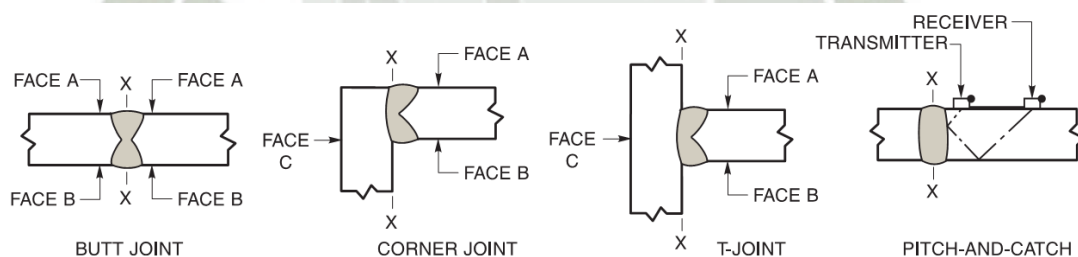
Identificación de Caras de la Junta Soldada
